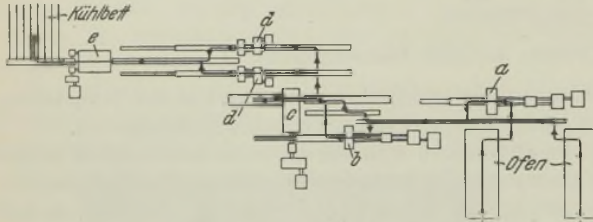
Lageplan einer Stopfenwalzwerksanlage.
